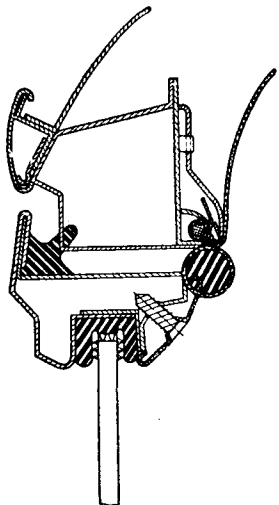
Безгвоздевое крепление обивки крыши и кантов.
